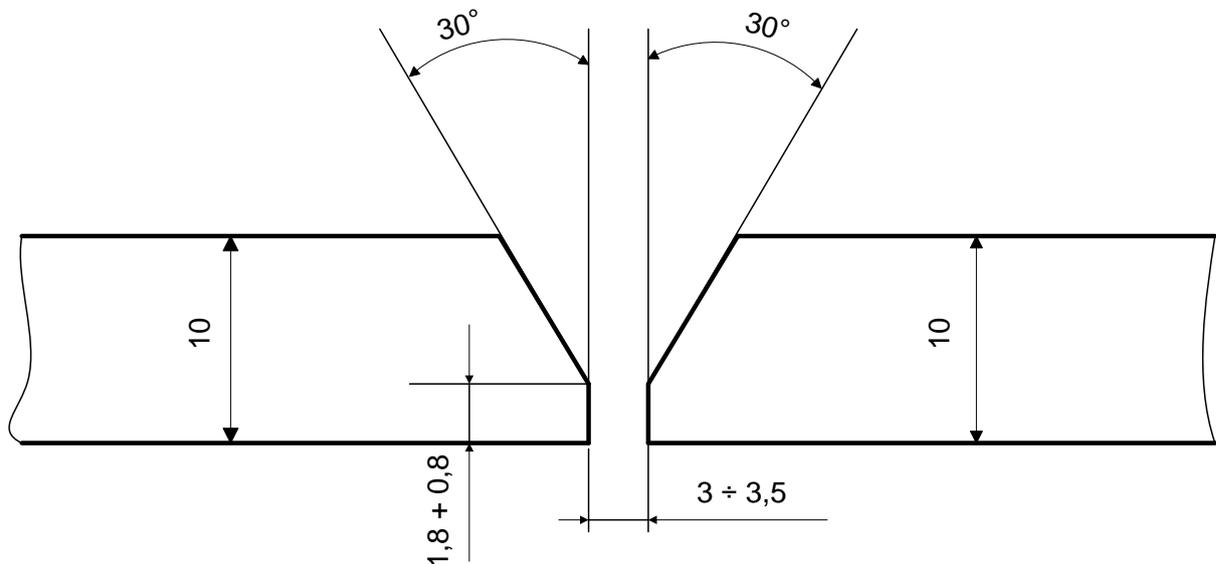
Разделка кромок труб для ручной дуговой сварки
